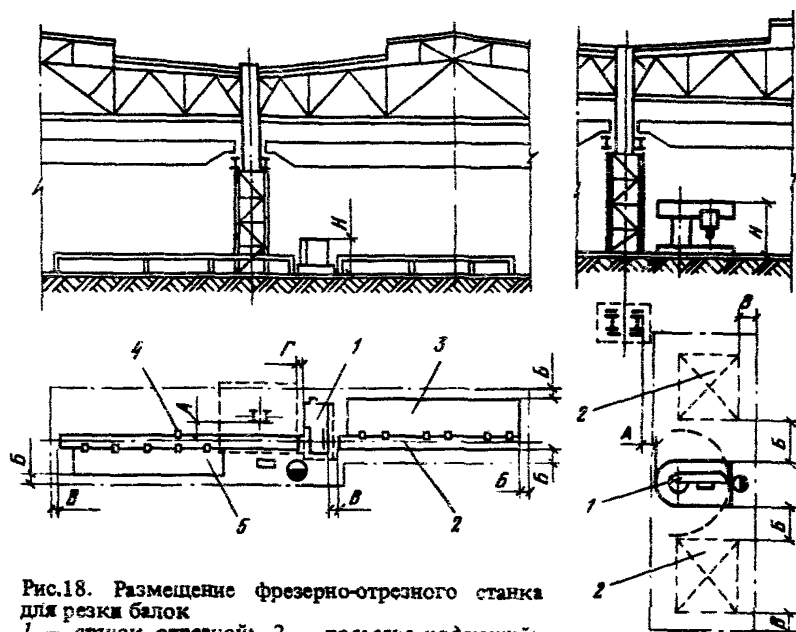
Размещение фрезерно-отрезного станка для резки балок
